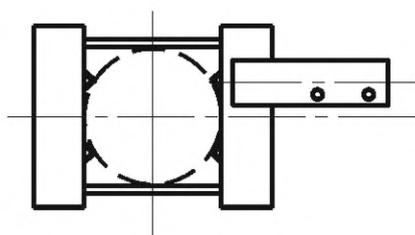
Основные размеры (вид сверху) кронштейнов, предназначенных для крепления двух- и трехполюсных разъединителей на напряжение 25 кВ
